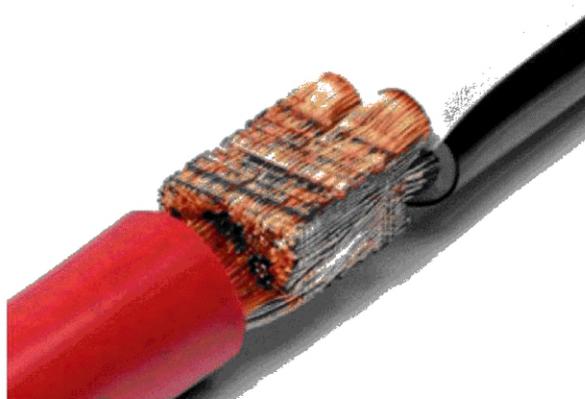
Двустороннее сваривание ультразвуковой сваркой медно-медное
